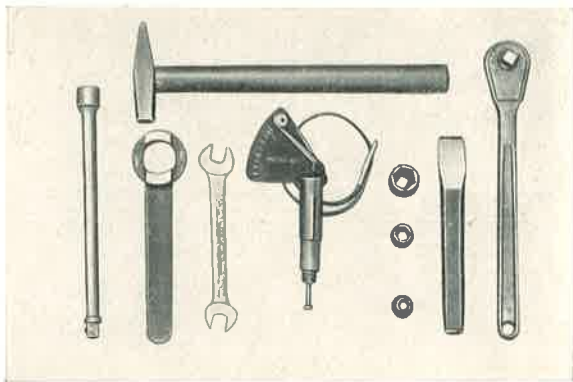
Zusammenstellung der Werkzeuge, die für die Arbeiten der Gruppe LAZ, (10 u. 22) gebraucht werden.
